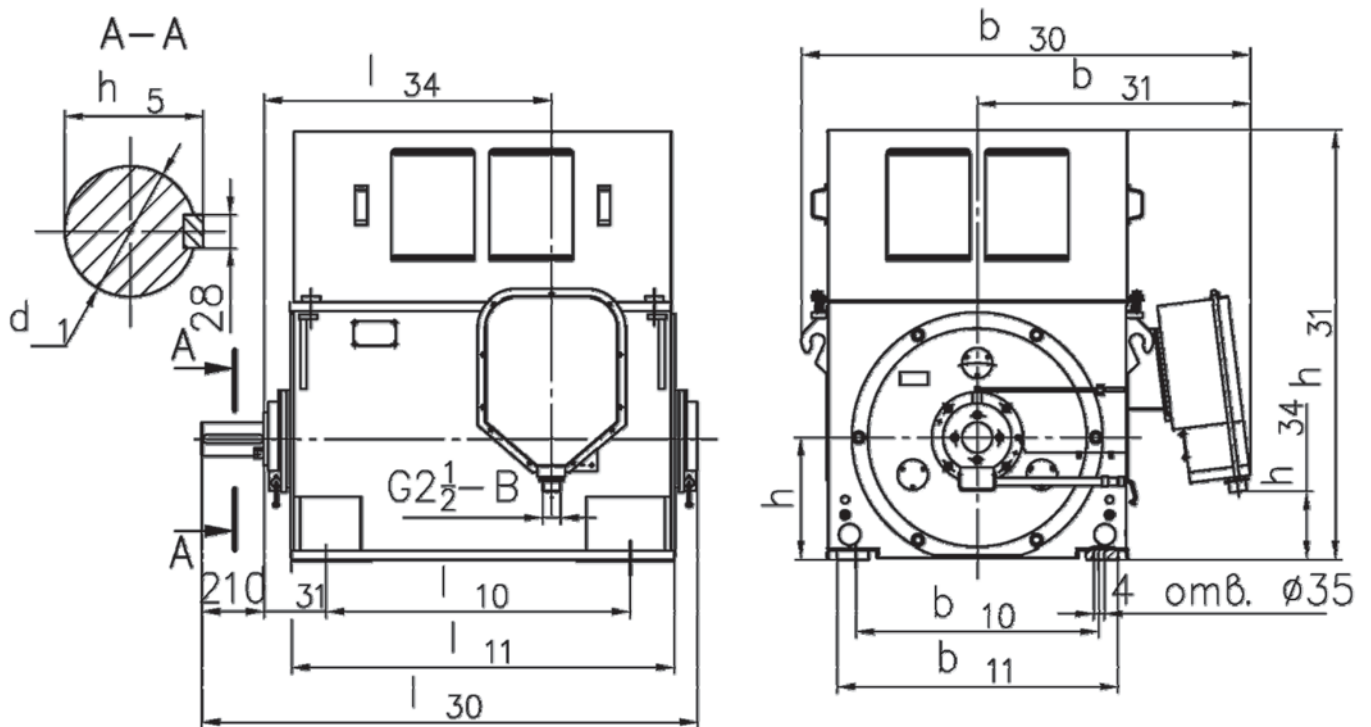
Электродвигатели серии А со сварной коробкой
